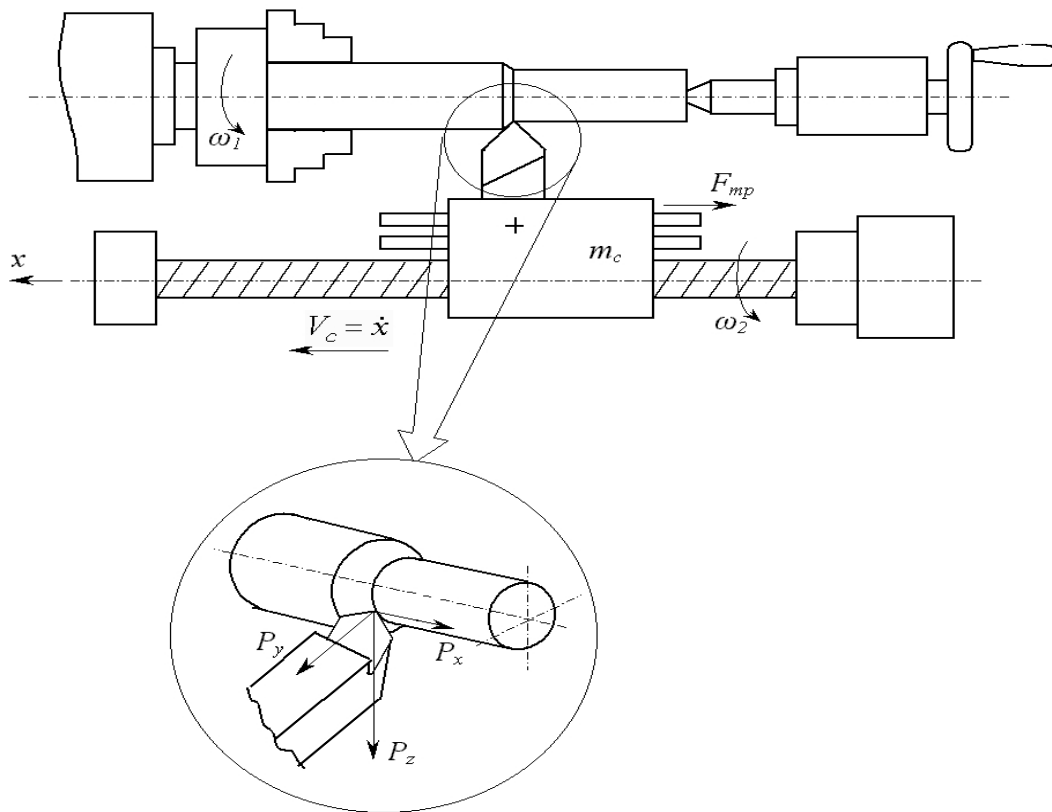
Конструктивная схема токарно-винторезного станка
